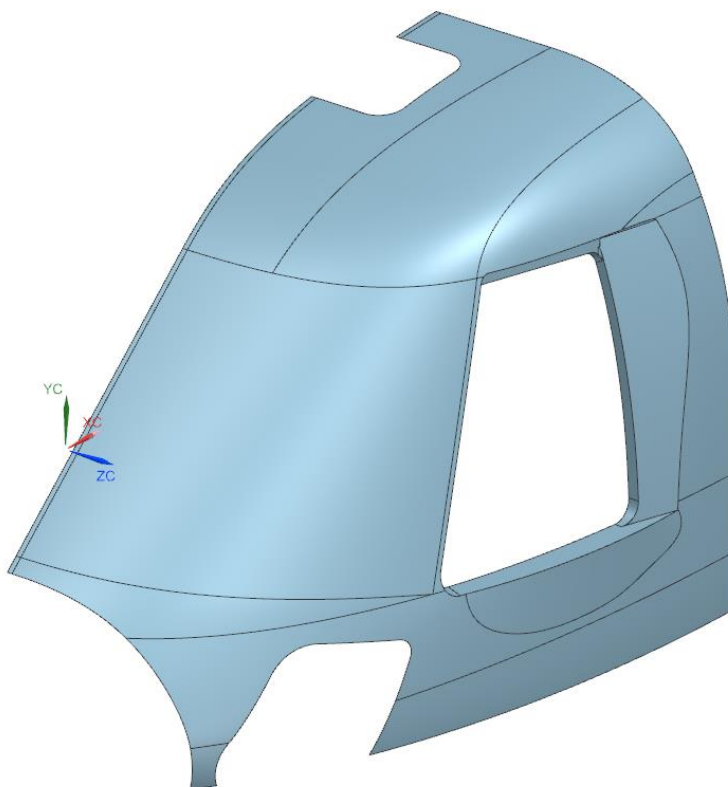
Поверхность внешней обшивки фонаря кабины пилотов
